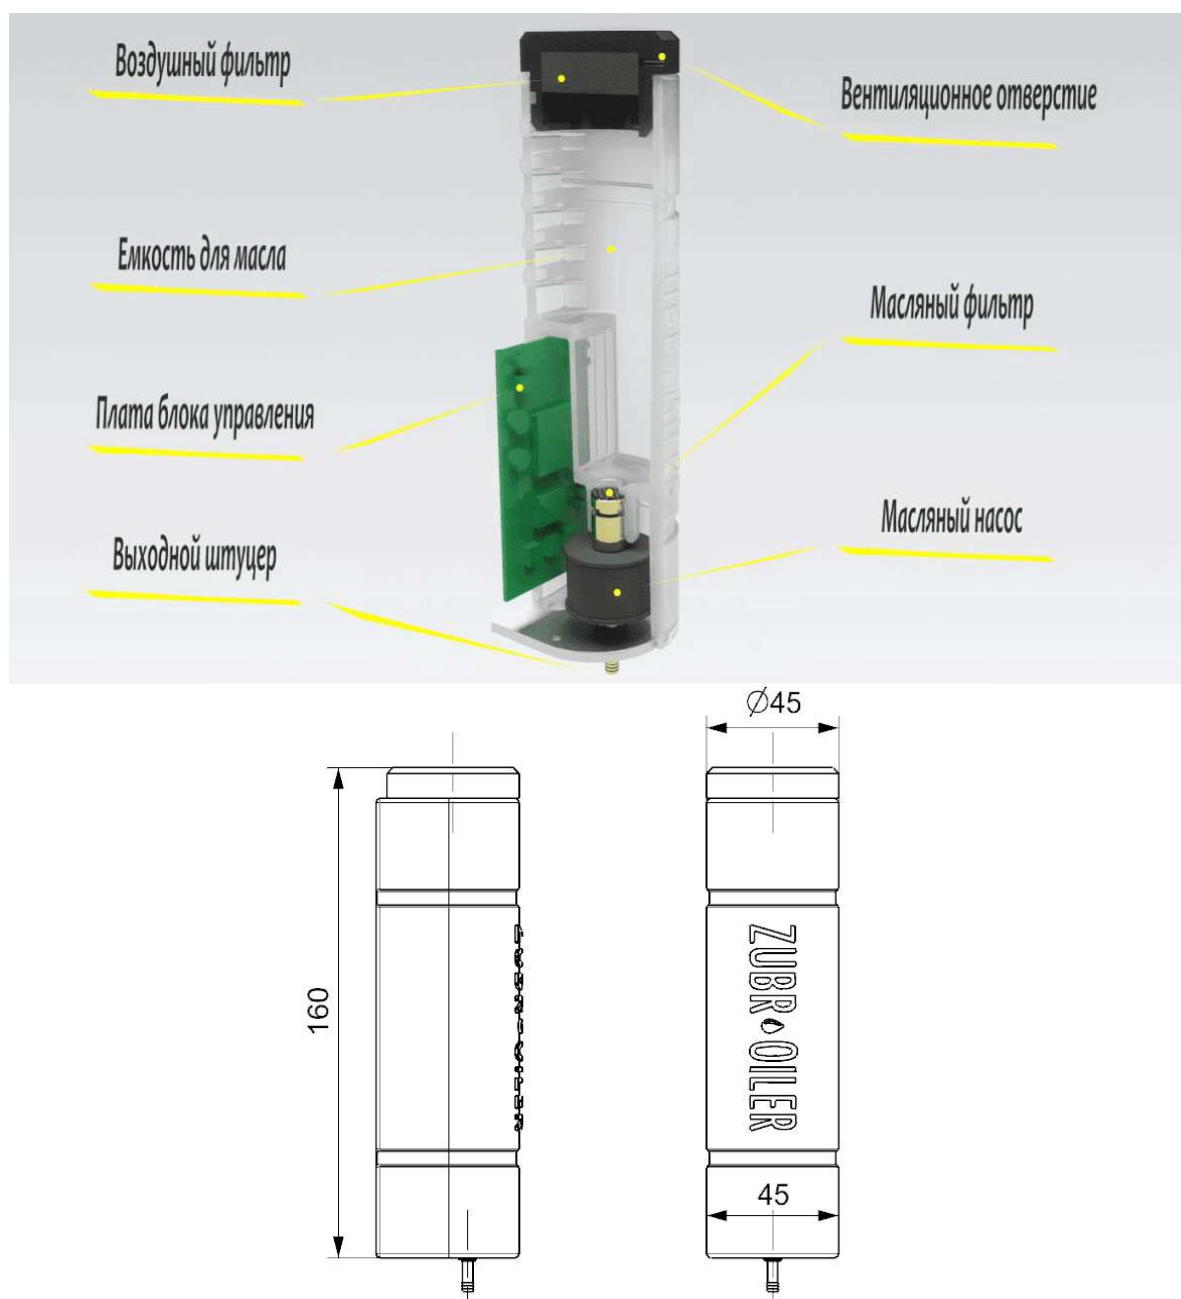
Схематическое изображение блока и габаритные размеры автосмазчика ZubrOiler
